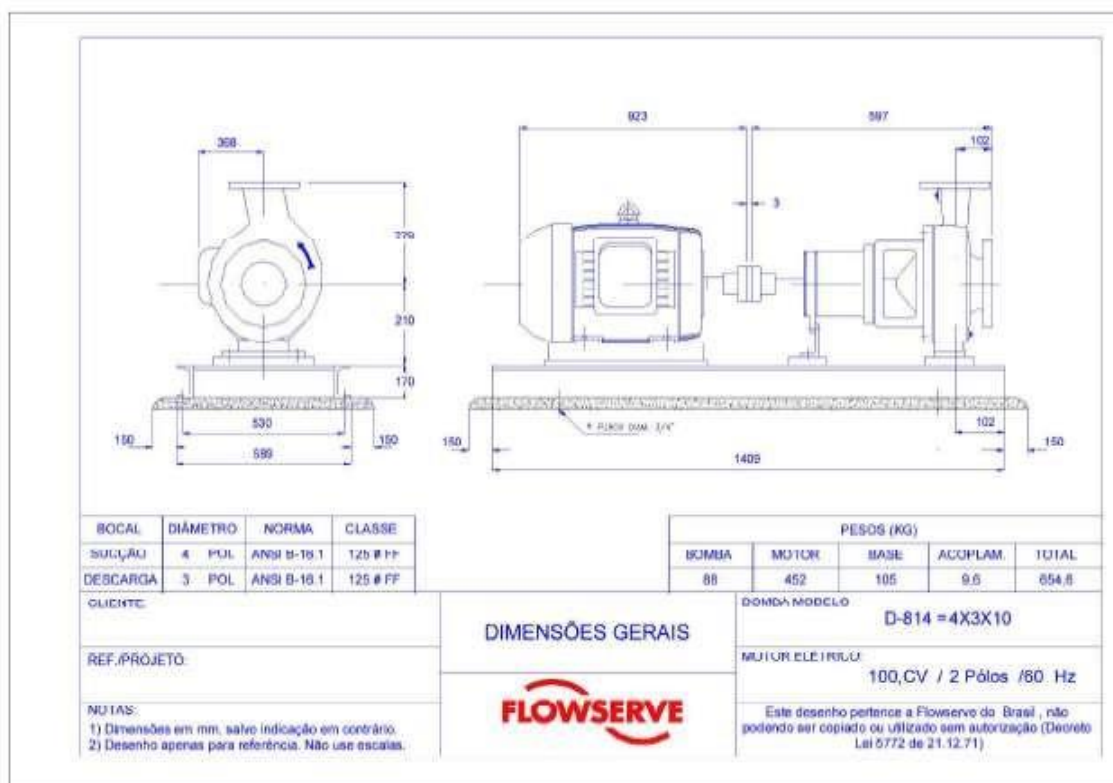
Dimensões do conjunto elevatório – motor de 100 CV
